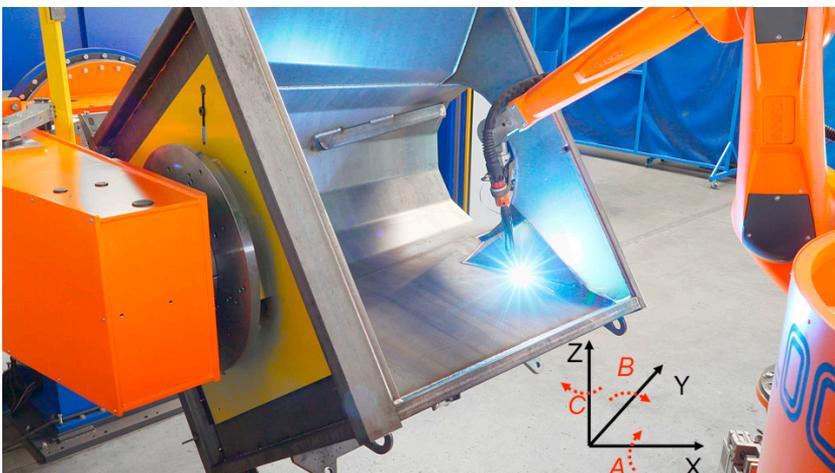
Schweißroboter mit gesteuerten Achsen (Foto: Cloos)
